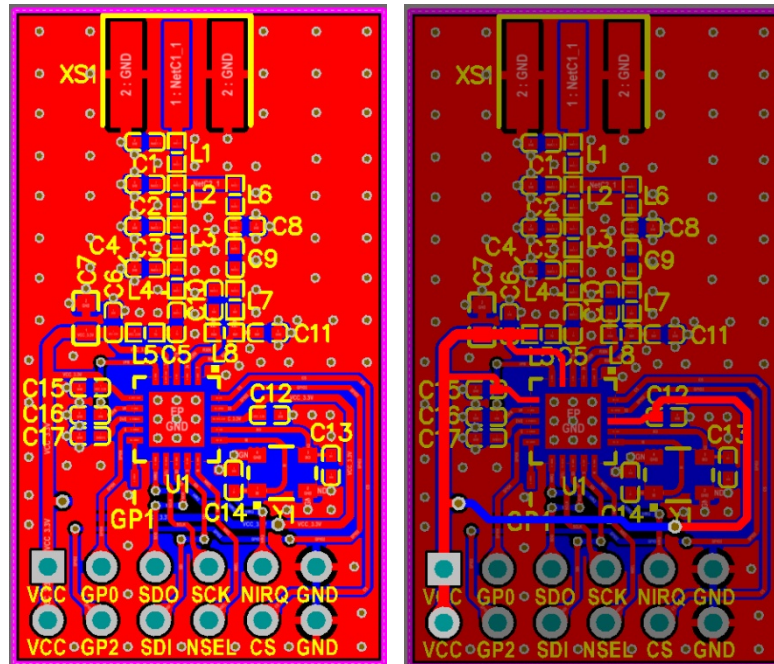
典型应用 PCB 图 (DC/DC OFF)
